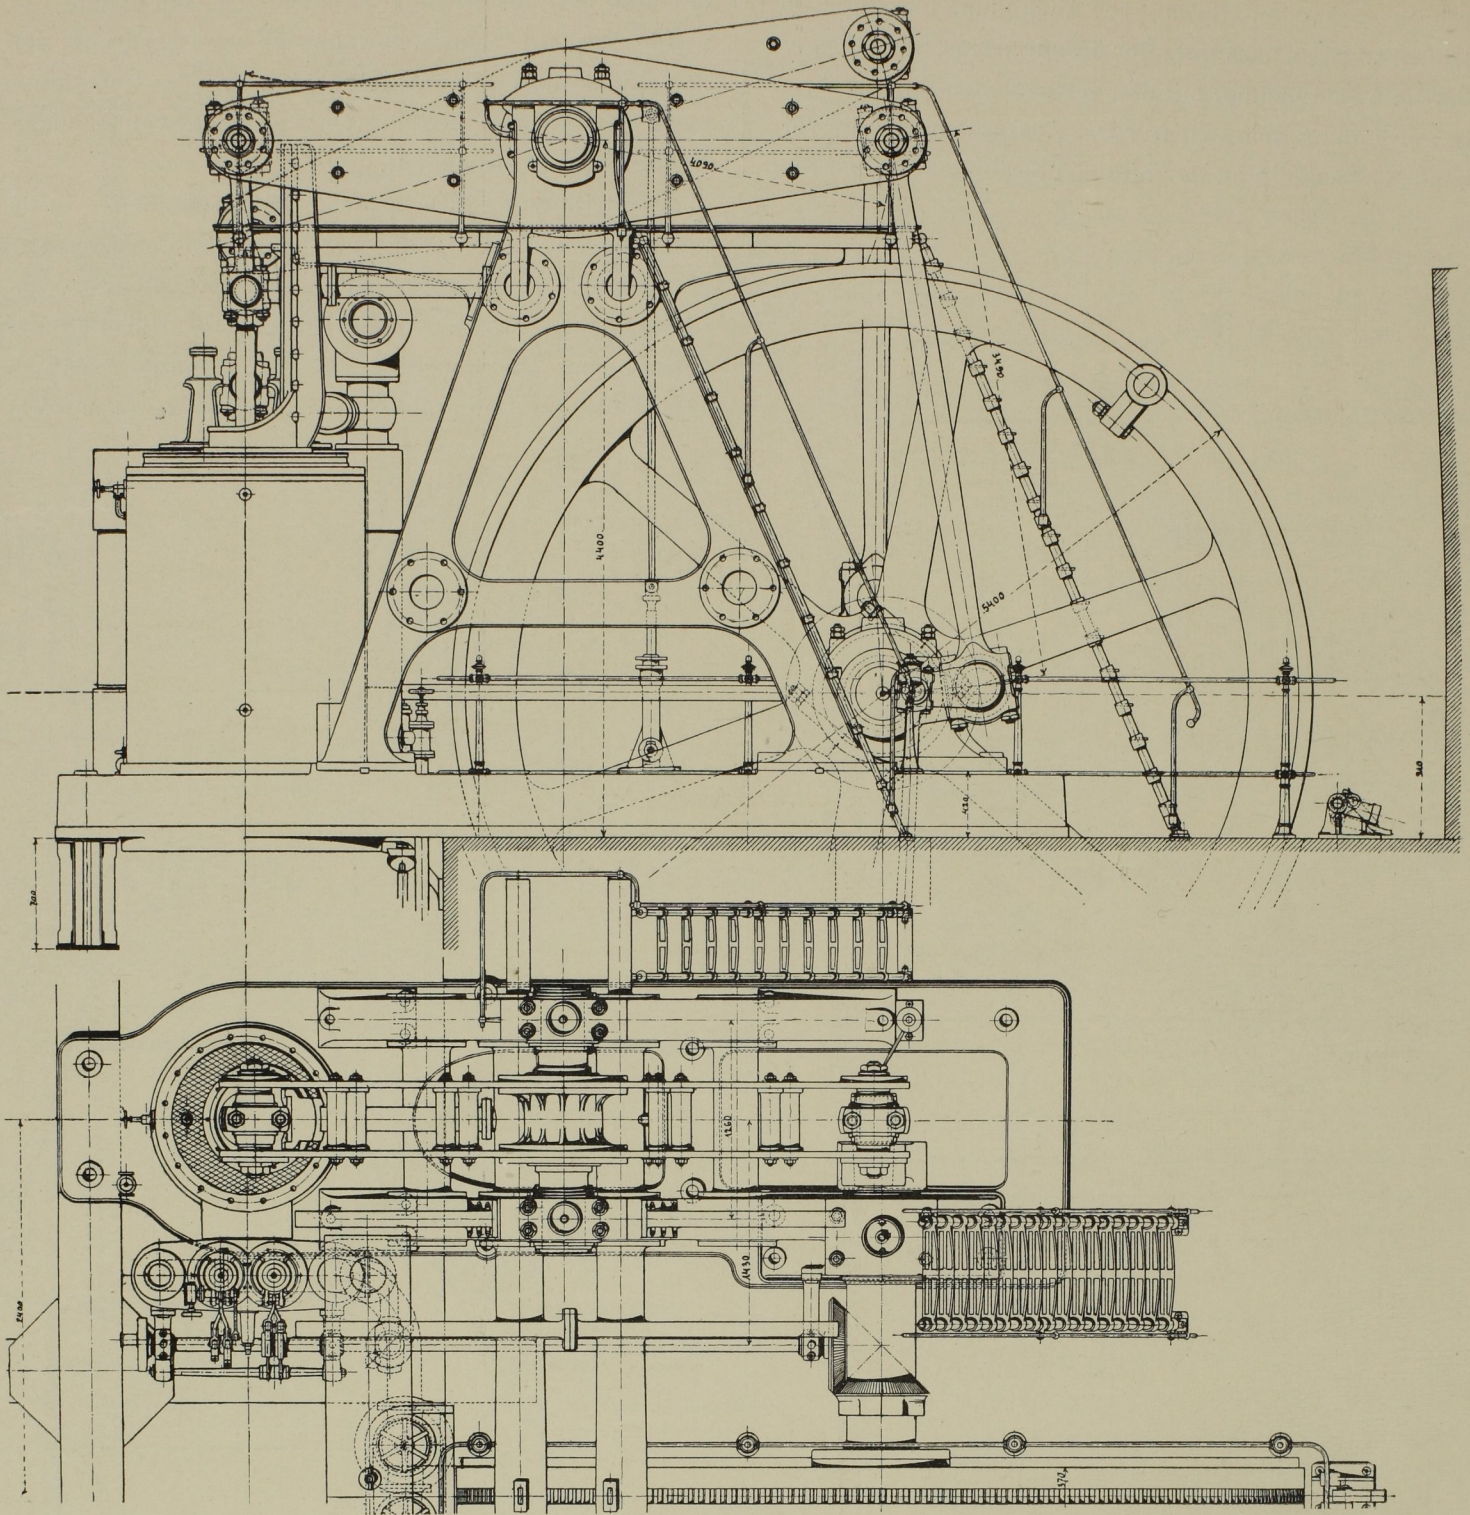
Seitenansicht und Grundriss der Dampfmaschine.
